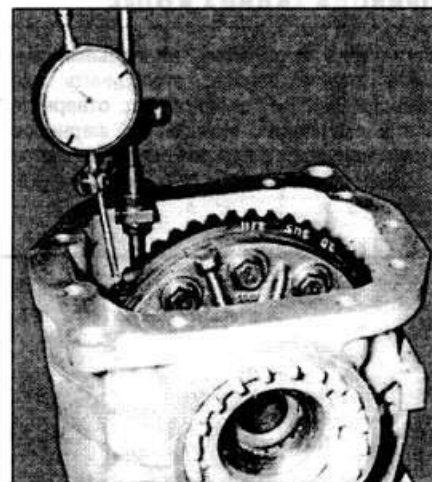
Проверка бокового зазора в зацеплении шестерен главной передачи
